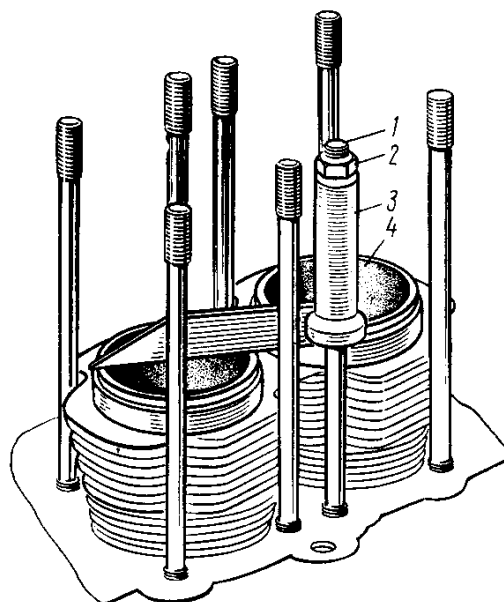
Приспособление для фиксации цилиндров на картере коленчатого вала
